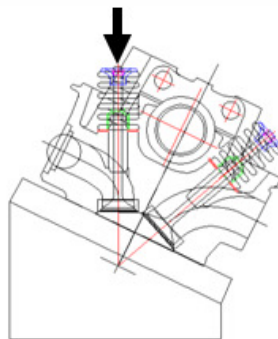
Proses OP 120 *Cylinder Head Machining
